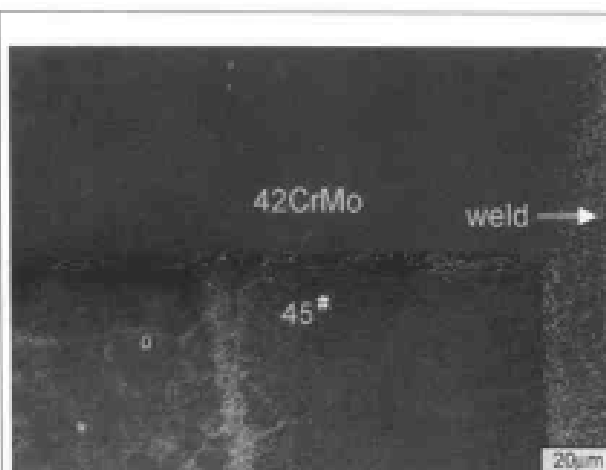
激光焊接, 42CrMo(上部材料)/45#(下部材料), CO<sub>2</sub> 激光, 功率 3200W, 焊接速度 2m/min
